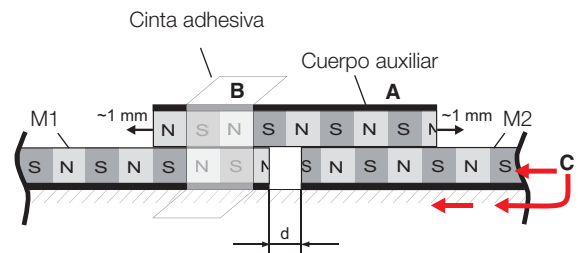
Cuerpo de medición M2 que se coloca debajo del cuerpo auxiliar, d = 4-10 mm
